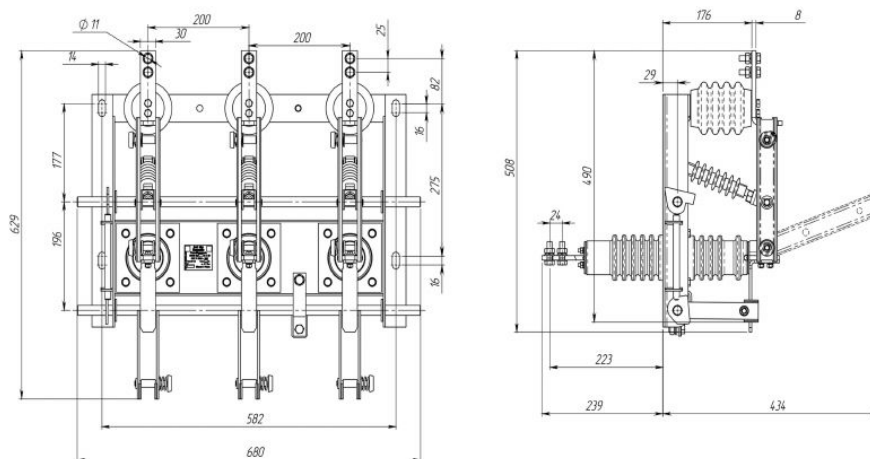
Разъединитель внутренней установки типа РВФЗ-10/630-II-У2 с заземляющими ножами со стороны шарнирных контактов, масса не более 30,88 кг
